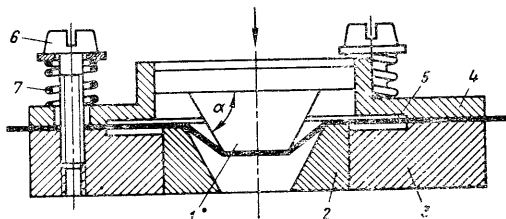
Пресс-форма для формовки мембран тарельчатой формы большой глубины
